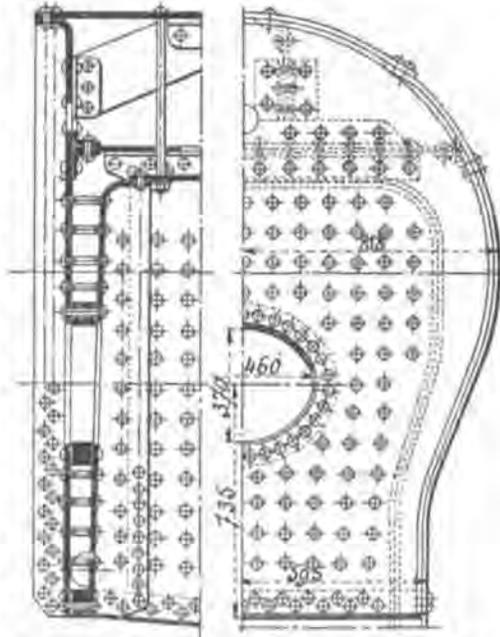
Disposition de la plaque arrière des chaudières des locomotives (groupe 450) du réseau *Adriatique*. L'emboutissage est tourné vers l'arrière ce qui permet de faire à la machine le rivetage de la pince d'attache avec le berceau.
